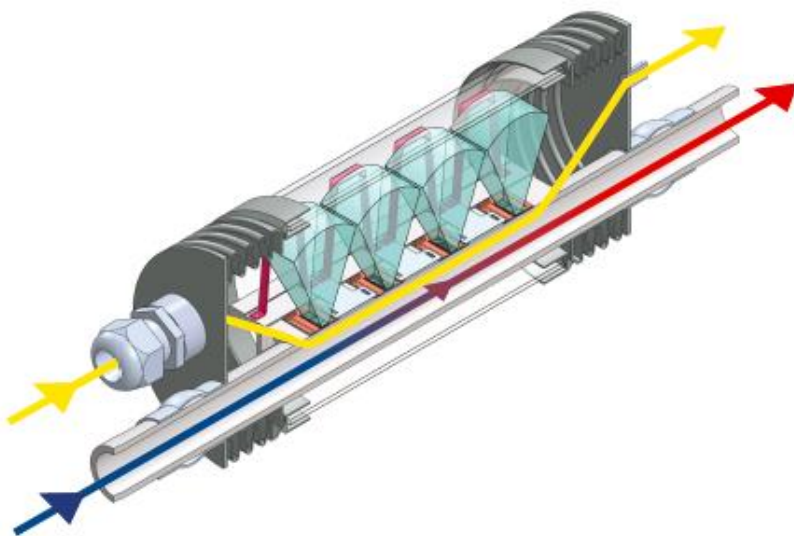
a: CAD-Schnitt durch Receiver Stand April 2017
